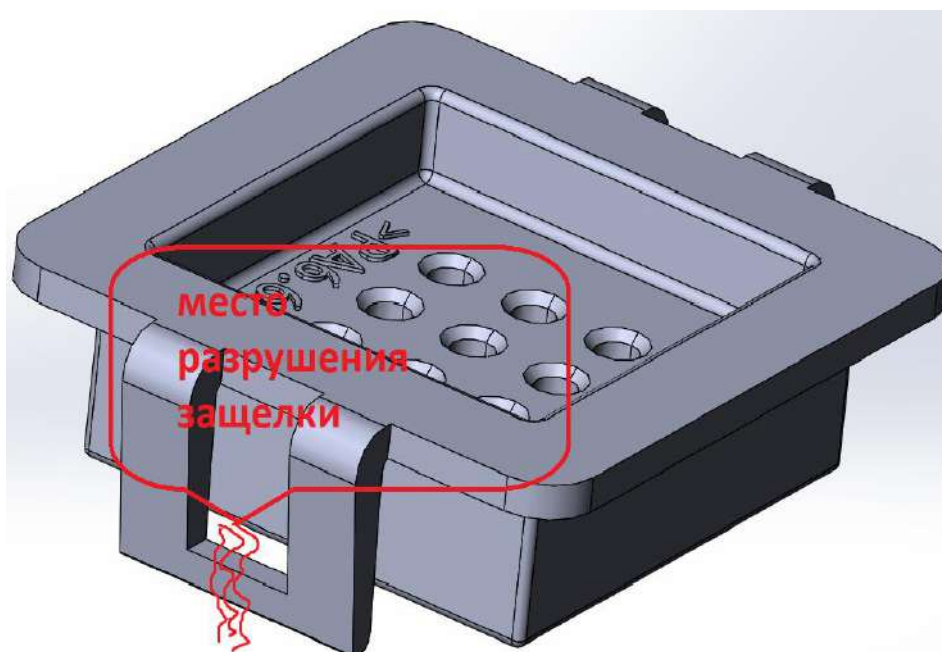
Место разрушения защёлки детали «Крышка блока»
